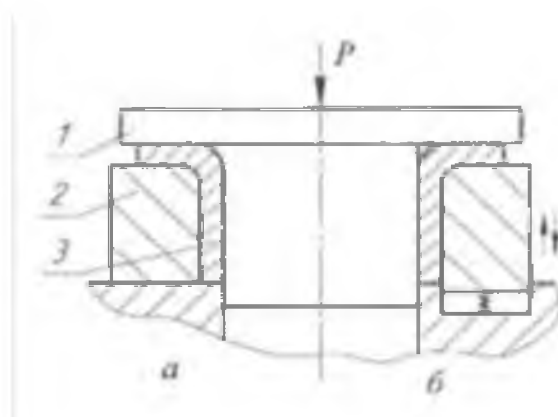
Схема раздачи (а) и осадки (б) трубной заготовки: 1 – пуансон; 2 – матрица; 3 – заготовка
